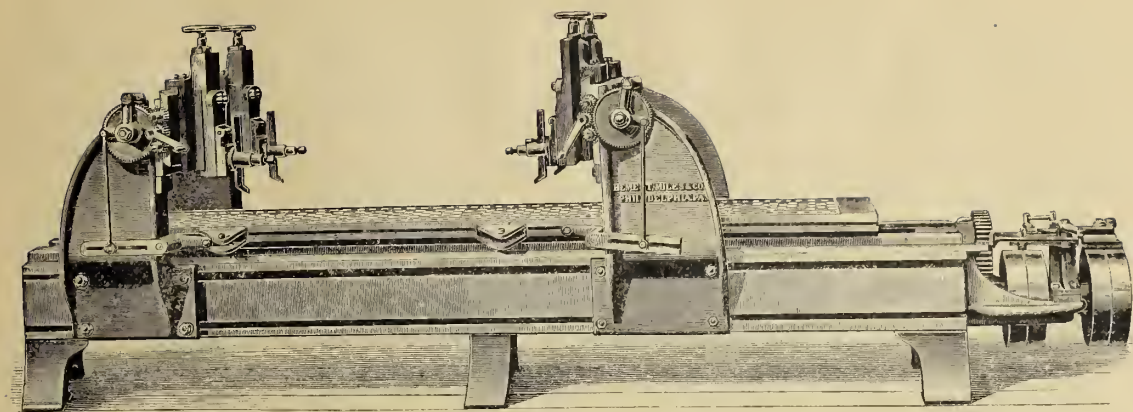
Machine horizontale à raboter les têtes de bielles.
